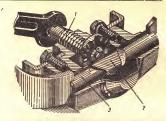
Регулировка вазора между колодками и тормозным барабаном автомобили ГАЗ-51А: J— регулировочный винт; z— плавающий сухарь; z— плавае.
